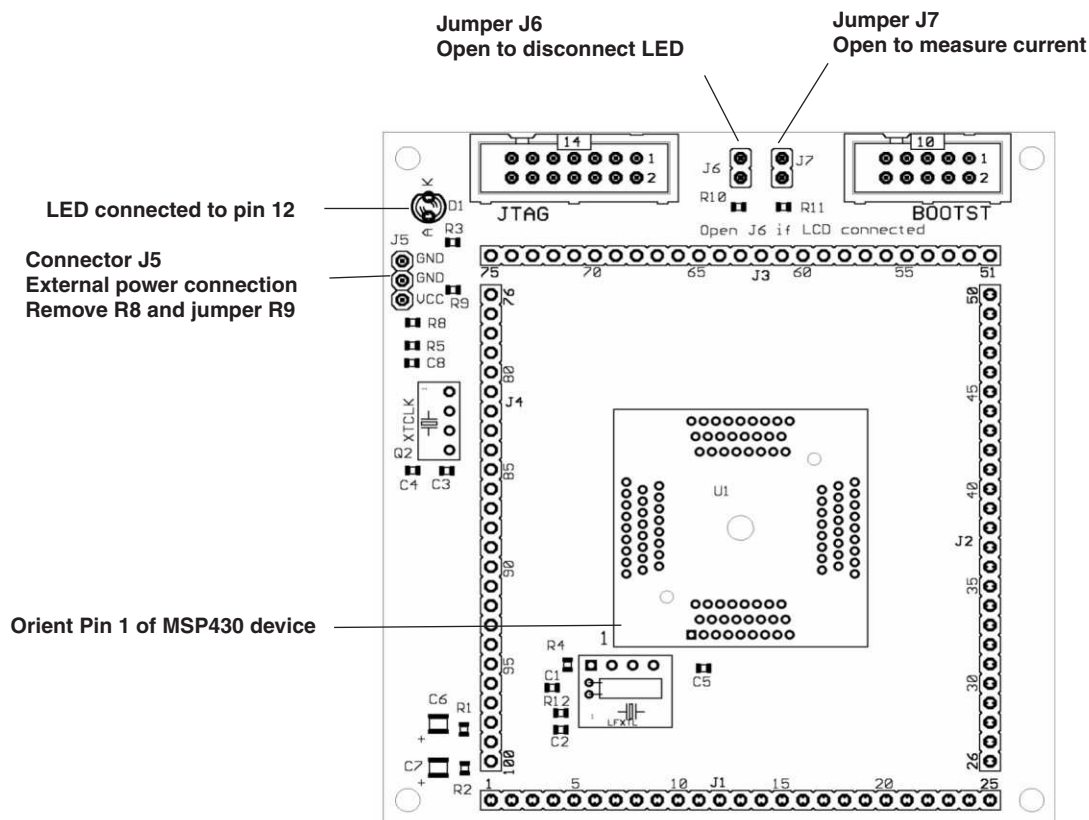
MSP-TS430PZ100 目标插座模块, PCB
